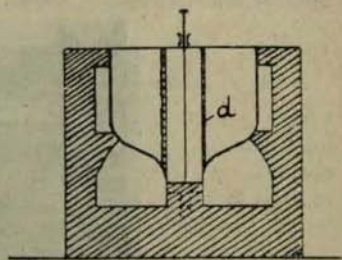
Dispositivo de De La Tour Du Breuil, corte transversal.
